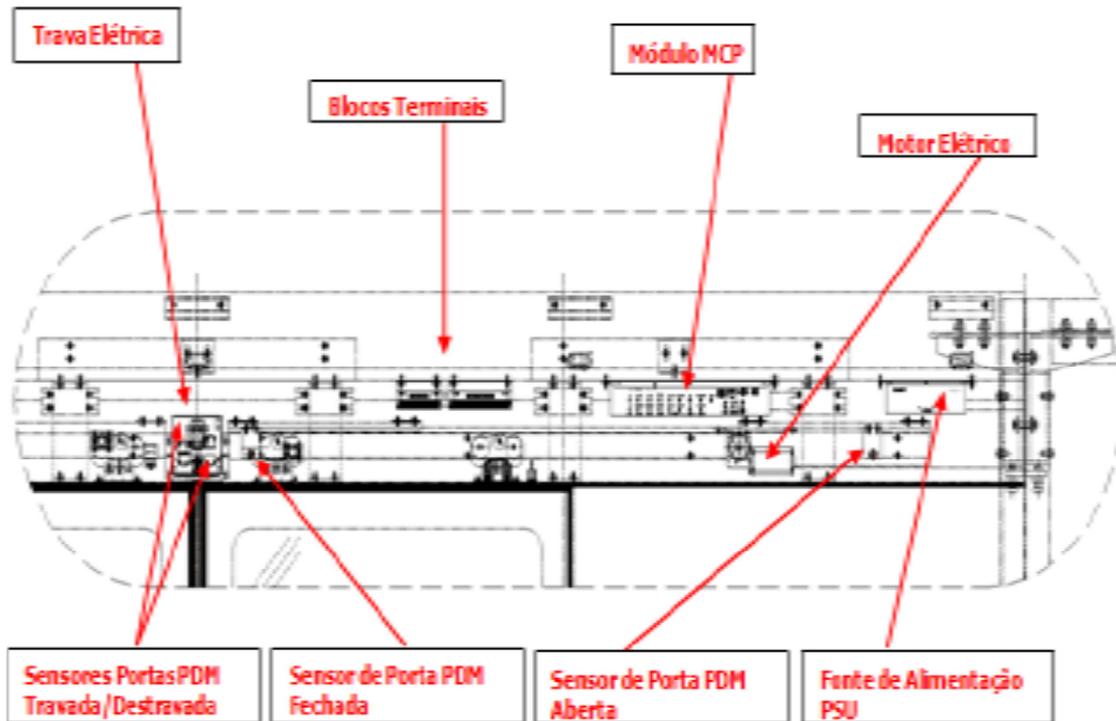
Equipamentos Que Compõem O Painel Header Box
